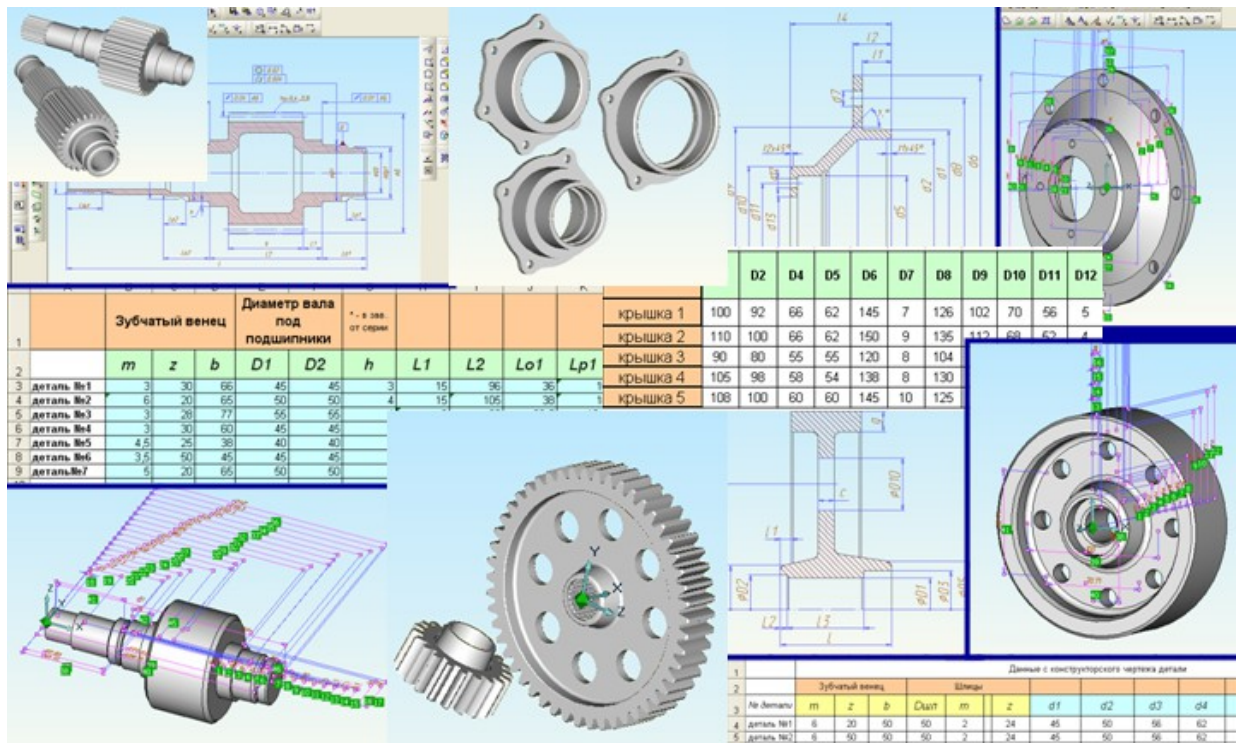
3D параметрические модели типовых деталей редуктора
